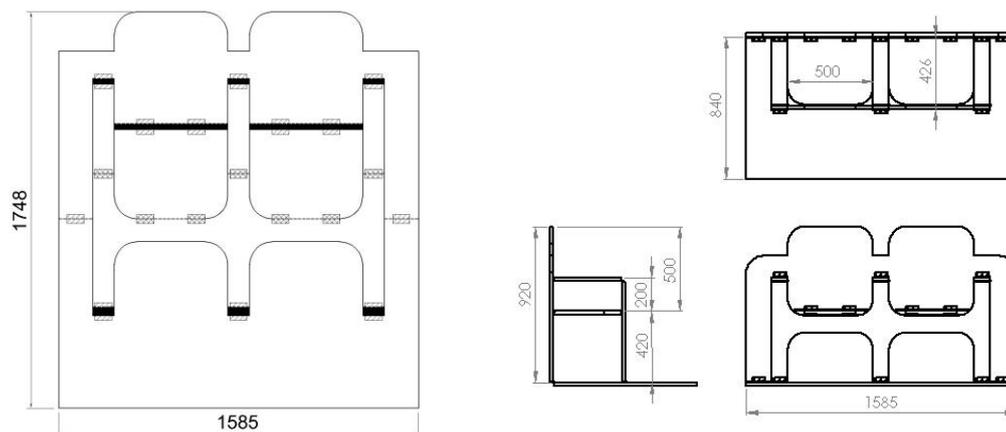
Medidas principais (em mm) do objeto planificado e aberto em 90°, respectivamente, elaborado pelos autores.
